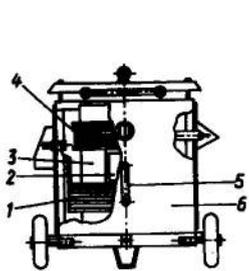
Зовнішній вигляд зварювального трансформатора СТШ-500
